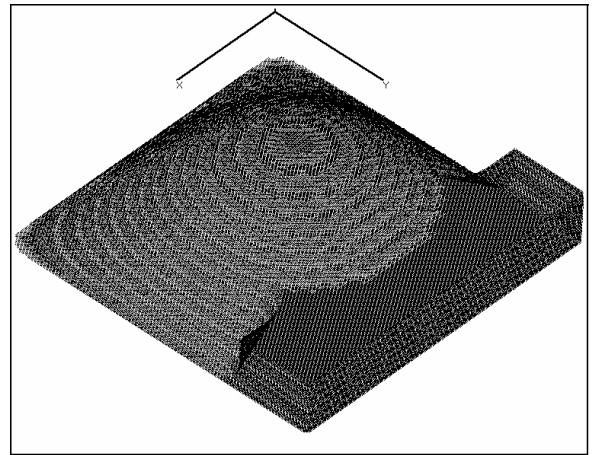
Поверхность заготовки, рассчитанная для случая обработки концевой фрезой по полученной траектории движения (обработка до положения по рис. 1)
